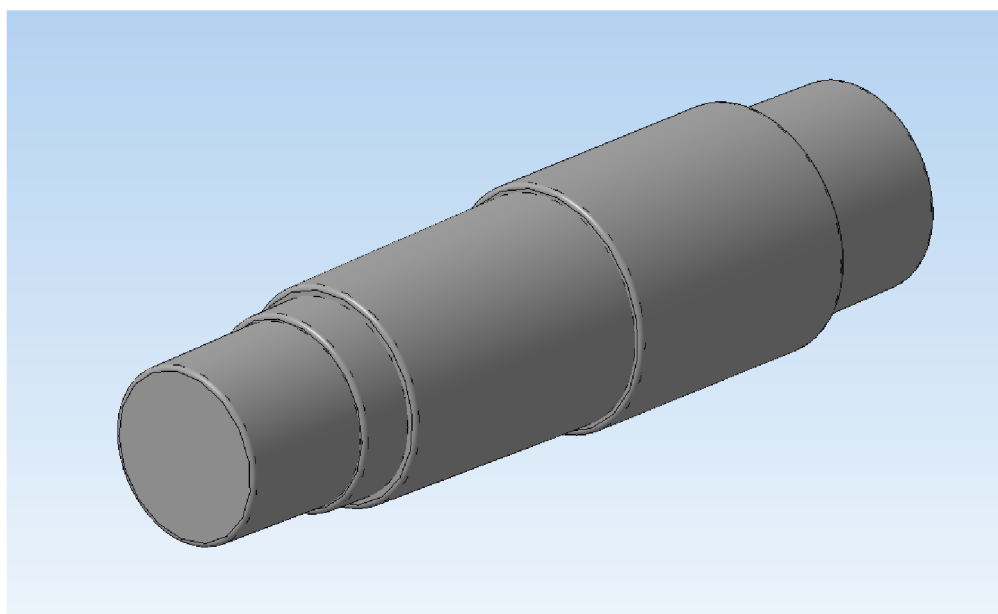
3D модель заготовки, що виготовлена ковкою на ГKM
